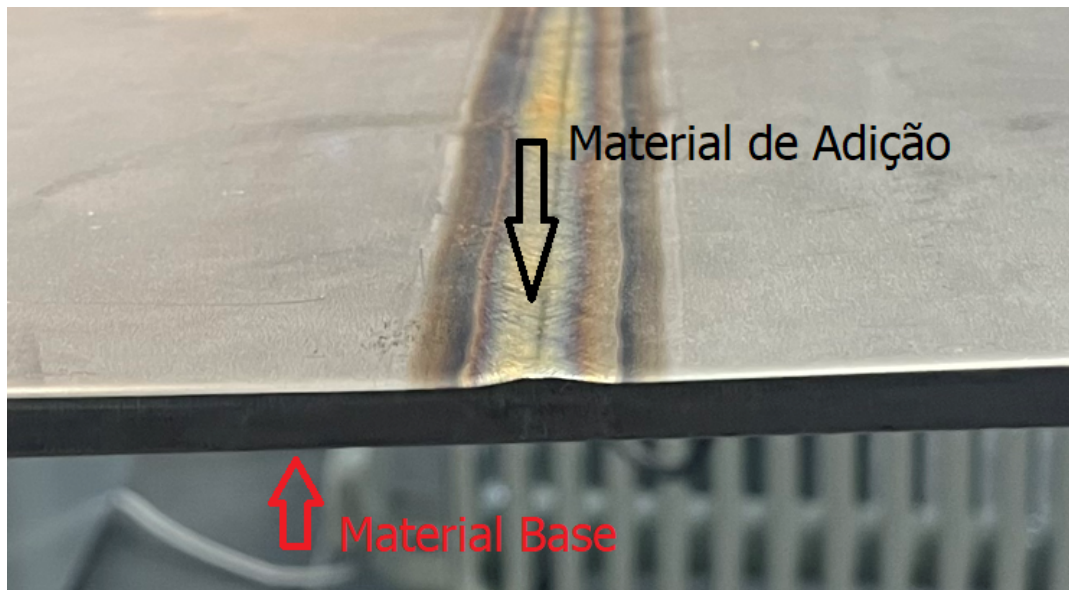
Ligação soldada por um processo TIG com material de adição.
